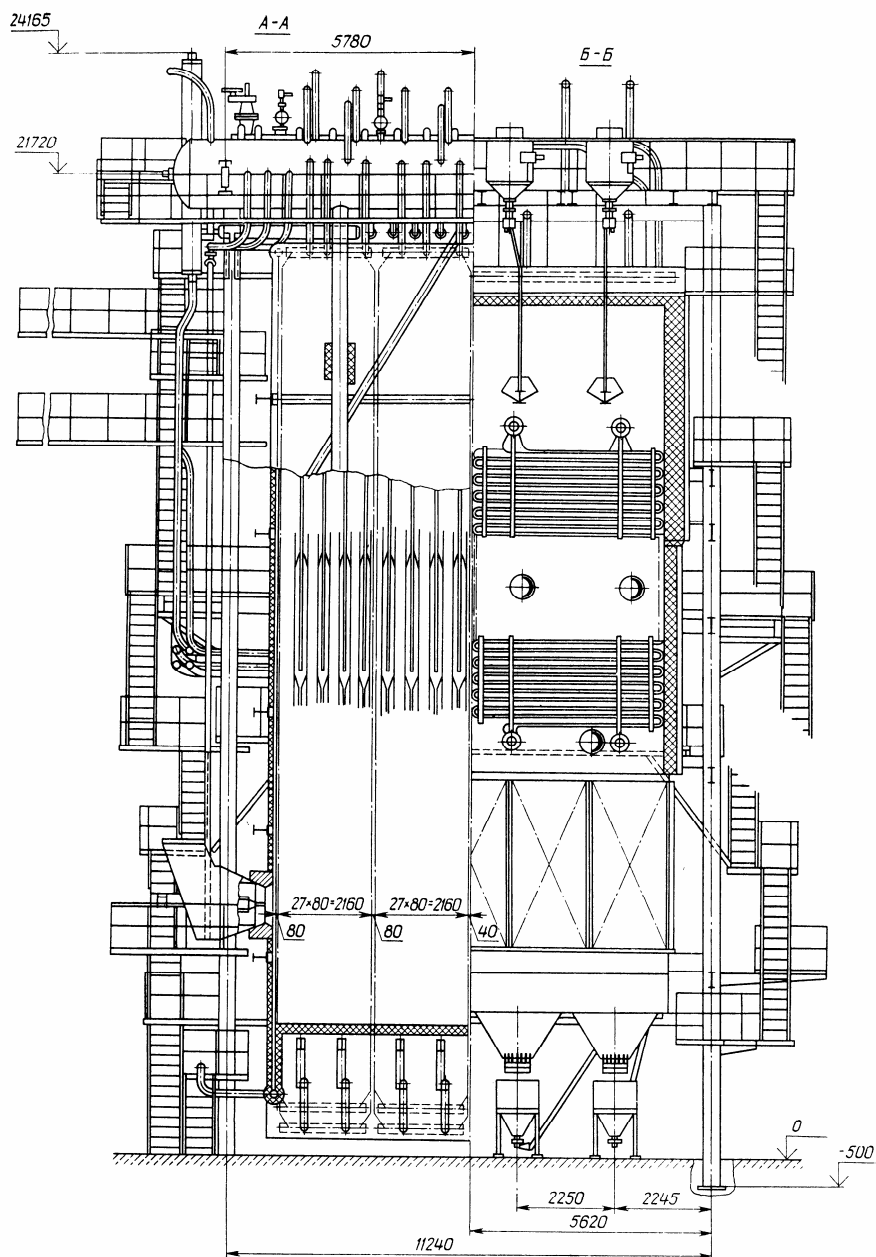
Поперечный разрез котла Е-160-1,4/2,4-250 ГМ (ТГМЕ-187)
